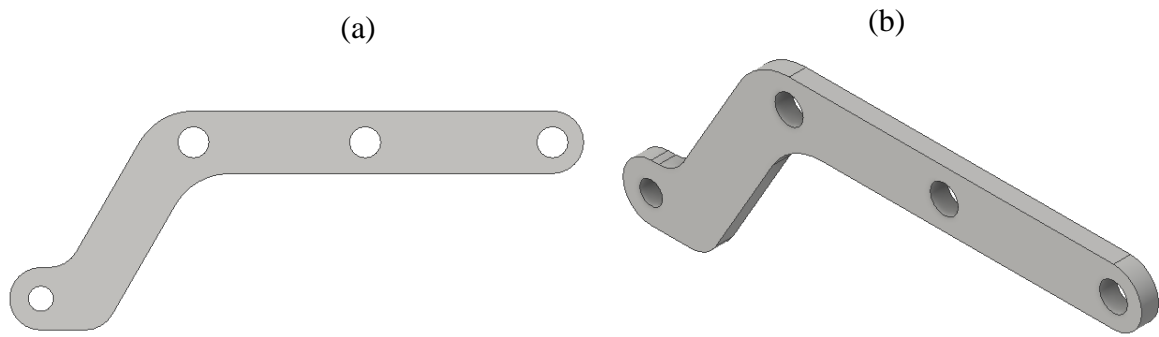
Pieza de unión espaldar/asiento/actuador lineal Vista Frontal (a) Isométrica (b)
